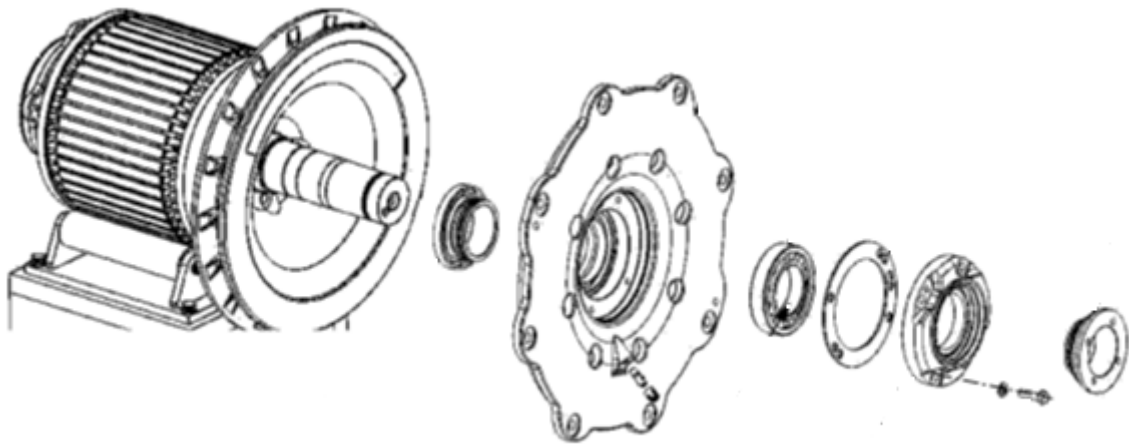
Rotor do Motor de Tração. Vista lado acoplamento.
